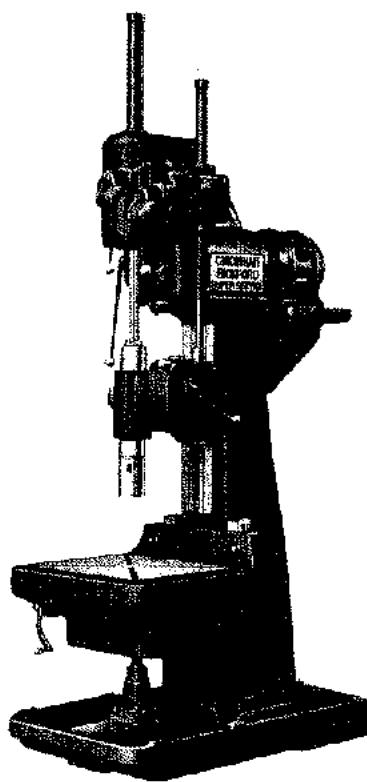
Taladradora pesada (Cincinnati Bickford Tool Co.)
